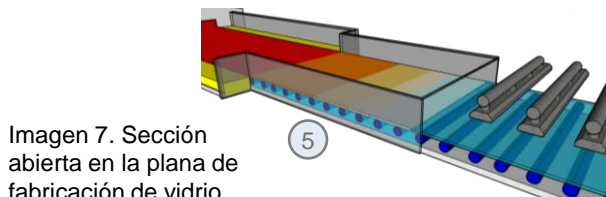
Sección abierta en la planta de fabricación de vidrio.
